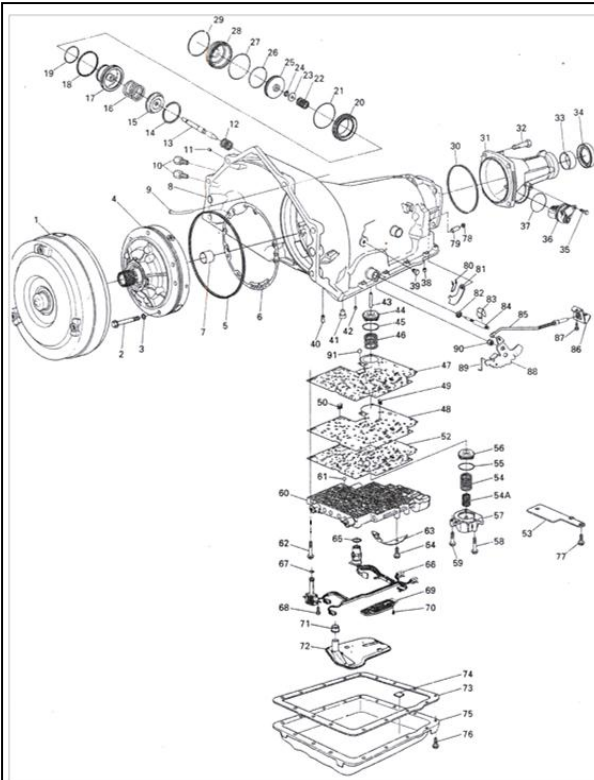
Despiece caja THM350 4L60-E parte externa
